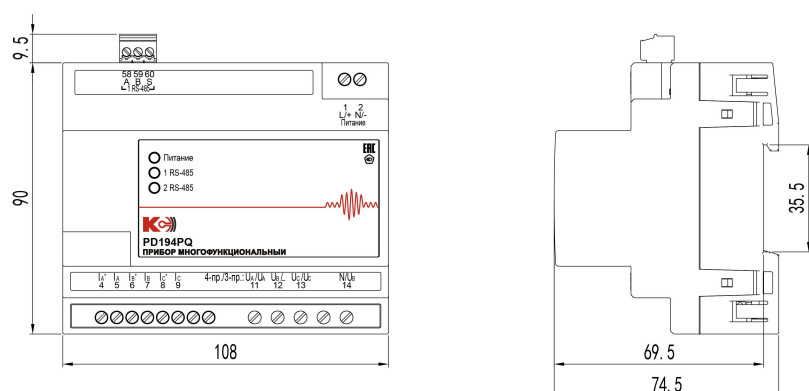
Внешний вид и размеры прибора PD194PQ-7K0T-00001
